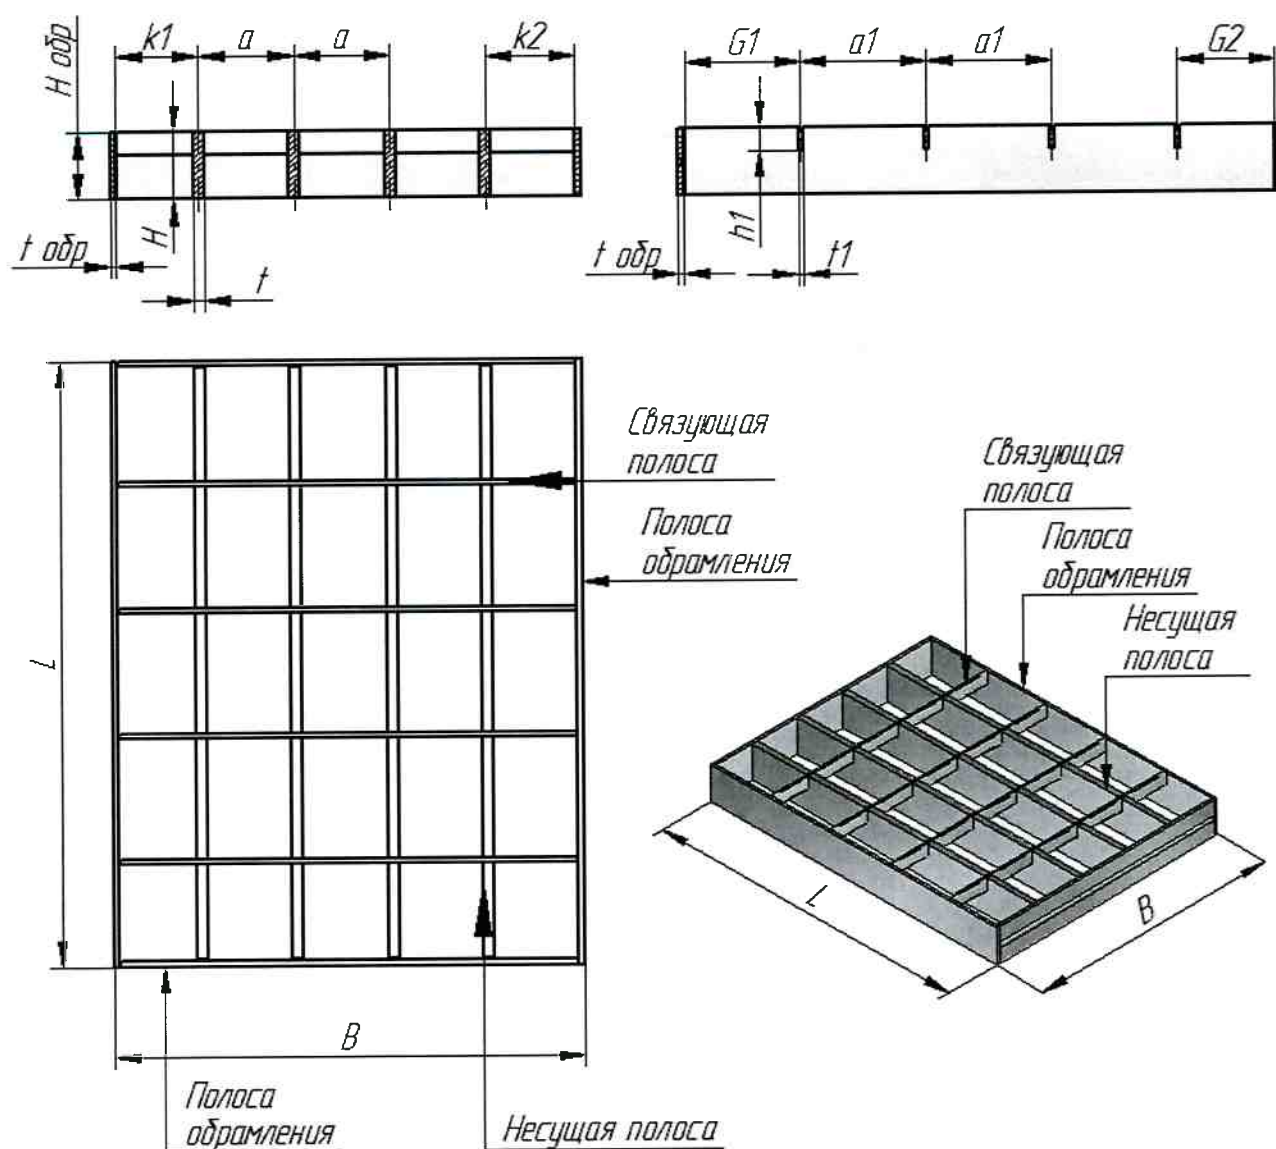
Обрамленный прессованный настил. Основные элементы конструкции
